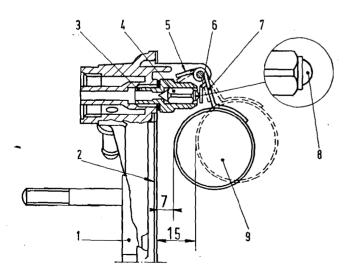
Schema per la livellatura del galleggiante del carburatore Weber tipo 26 IMB 4.
